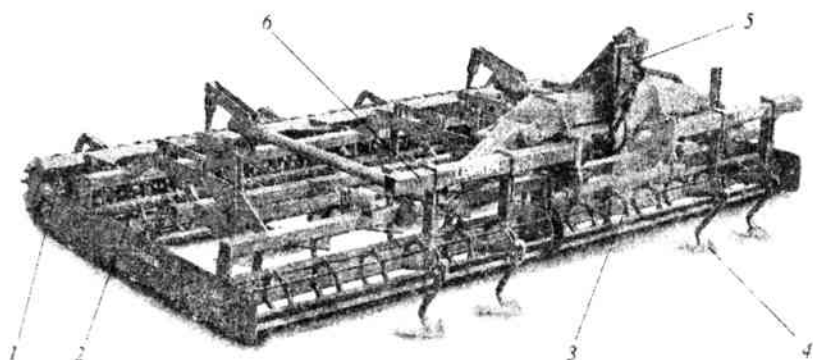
Многоцелевое орудие для предпосевной подготовки почвы «Компактор» фирмы Lemken: 1 – кольчатый каток; 2, 3 – планчатые катки; 4 – пассивный рабочий орган; 5 – навесное устройство; 6 – рама
